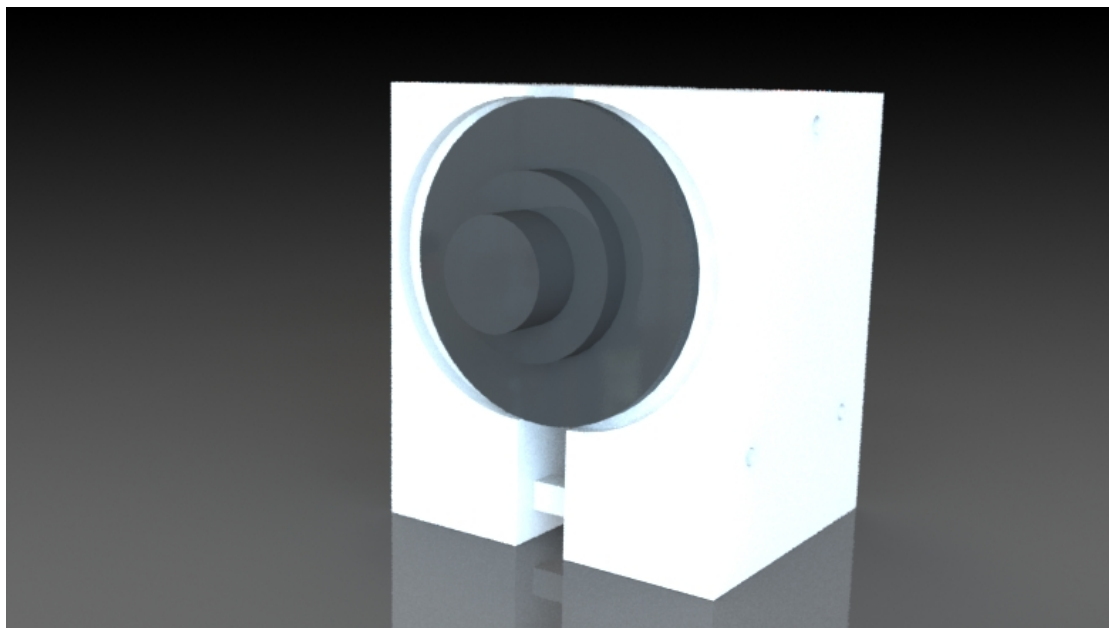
Ensamblaje explosionado de las piezas que abrazan al anillo rozante 1.
